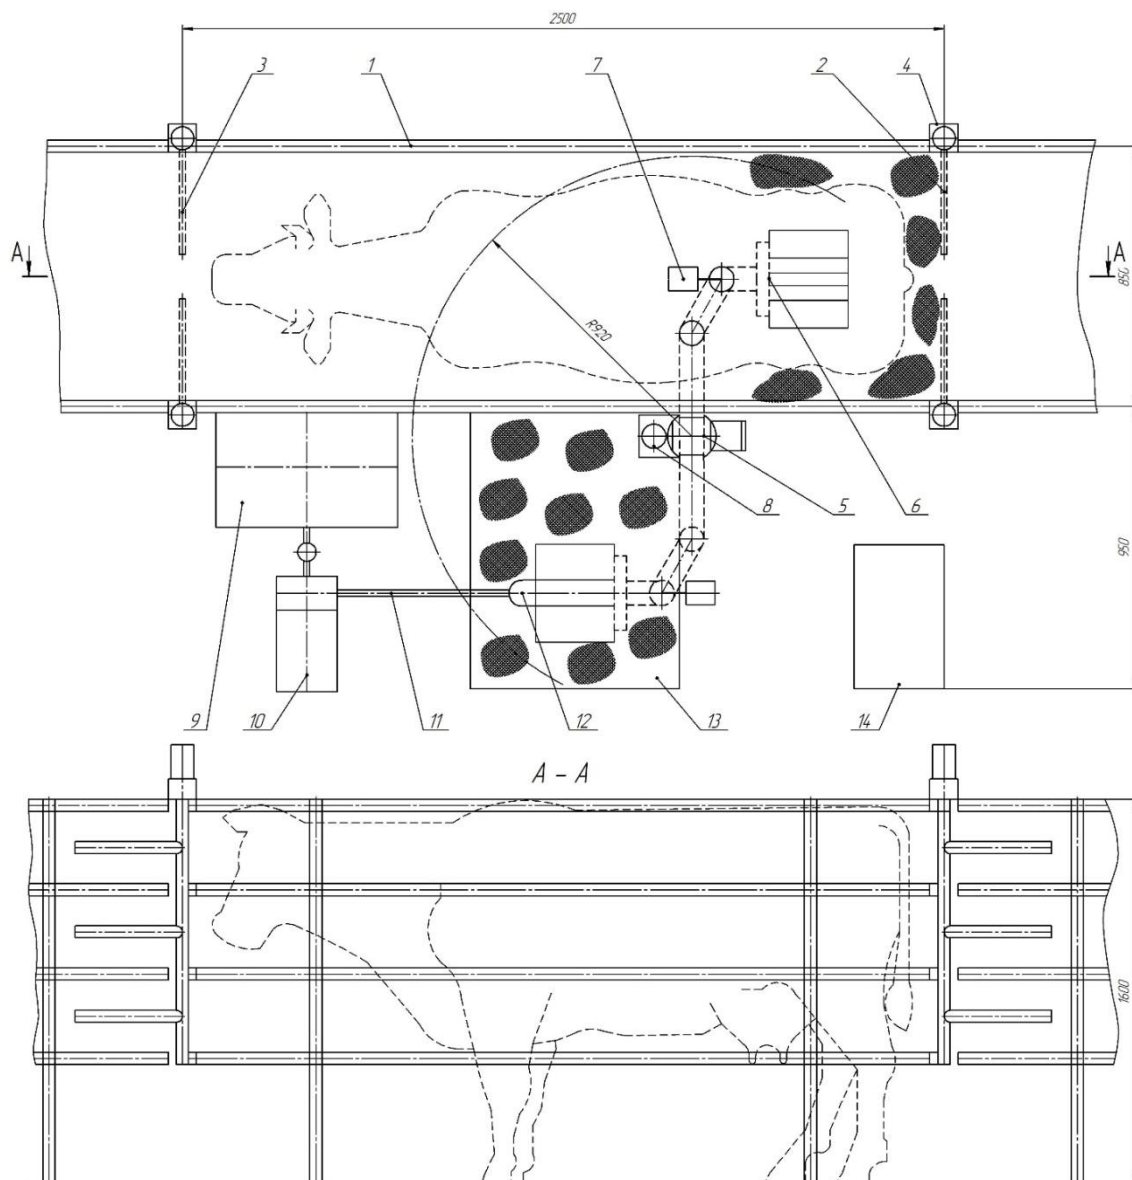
Схема установки преддоильной подготовки вымени:
